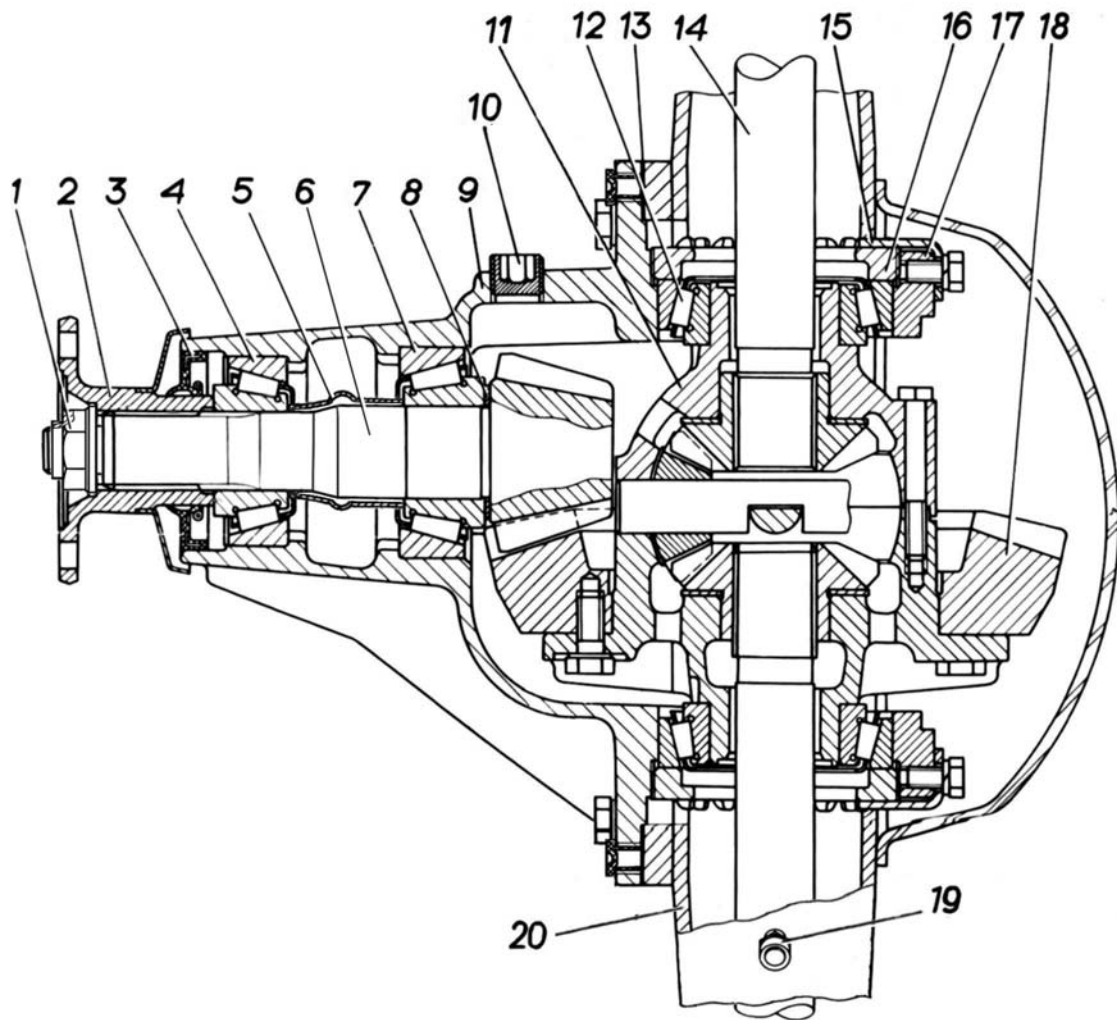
Задний мост (средняя часть): 1 – гайка; 2 – фланец ведущей шестерни; 3 – манжета; 4, 7 и 12 – подшипники; 5 – распорная втулка; 6 – ведущая шестерня; 8 – регулировочное кольцо; 9 – картер редуктора; 10 – пробка маслозаливного отверстия; 11 – дифференциал; 13 – прокладка; 14 – полуось; 15 – стопорная пластина; 16 – гайка подшипников дифференциала; 17 – крышка подшипника дифференциала; 18 – ведомая шестерня; 19 – сапун; 20 – картер заднего моста
